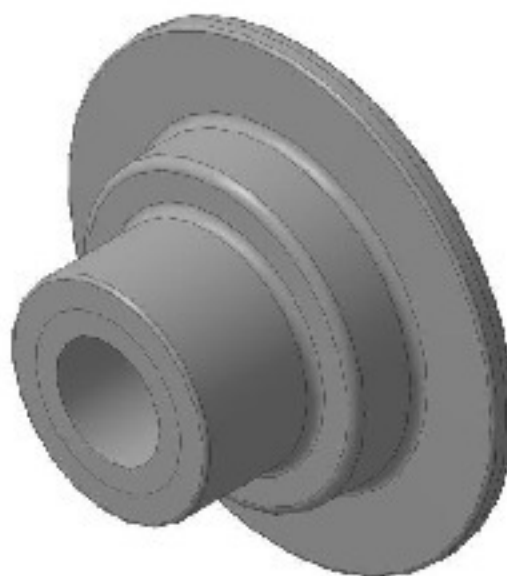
3D-модель заготовки виготовленої штампуванням на ГП
